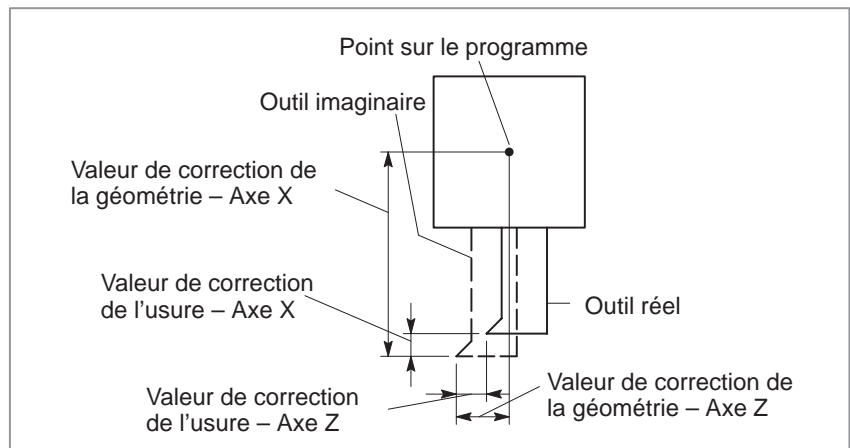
Correction de géométrie d'outil par rapport à la correction d'usure d'outil
